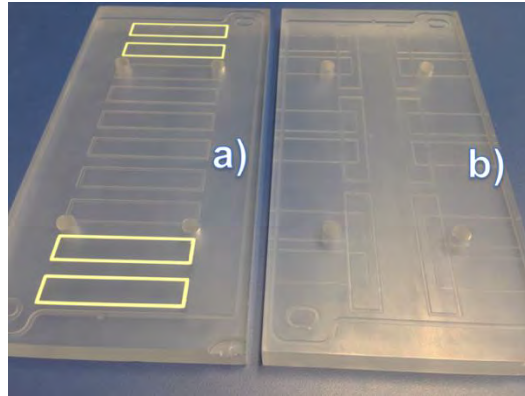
a) Molde para la primera configuración; b) Molde con espacio para fabricar sello con cable de Pt inmerso.
